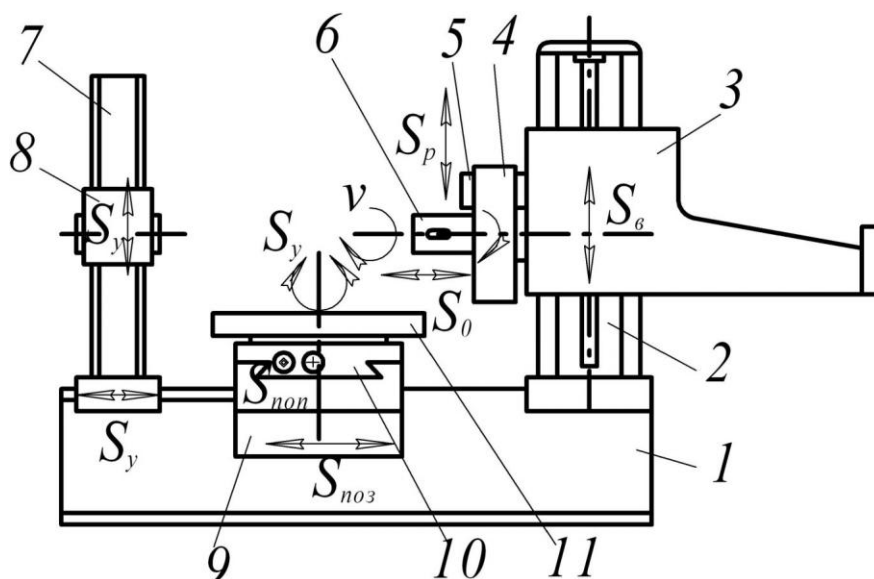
Загальний вигляд горизонтально-розточувального верстата
